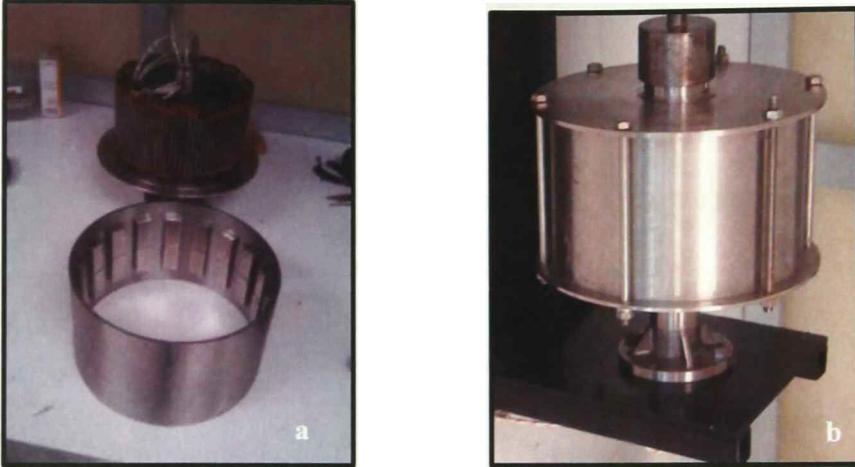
GSIP: a) Rotor y Estator, b) Ensamble
